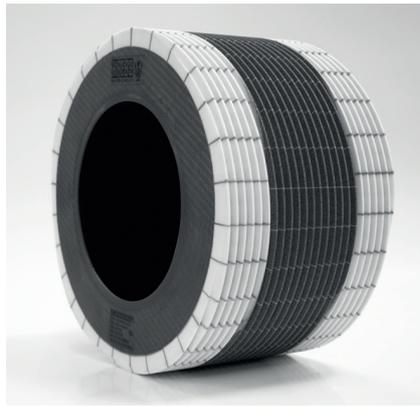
CBN-Schleifschnecken auf einem Carbon Grundkörper sind wiederbelegbar
